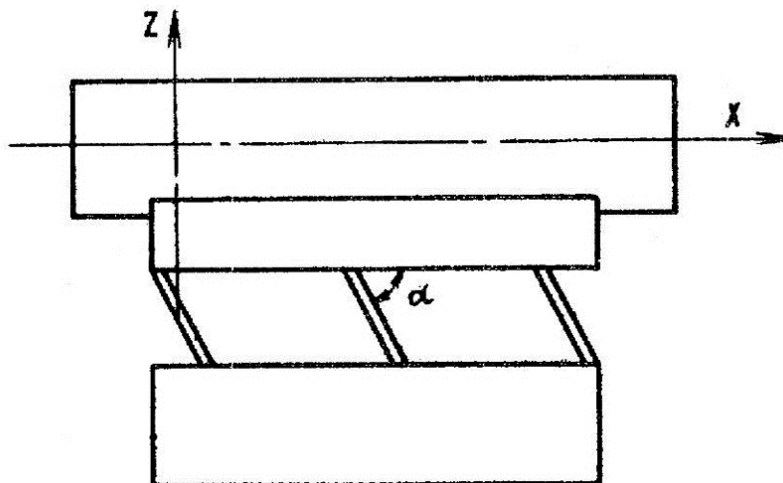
Опорный нож бесцентрово-шлифовального станка по А.с. СССР № 921798
